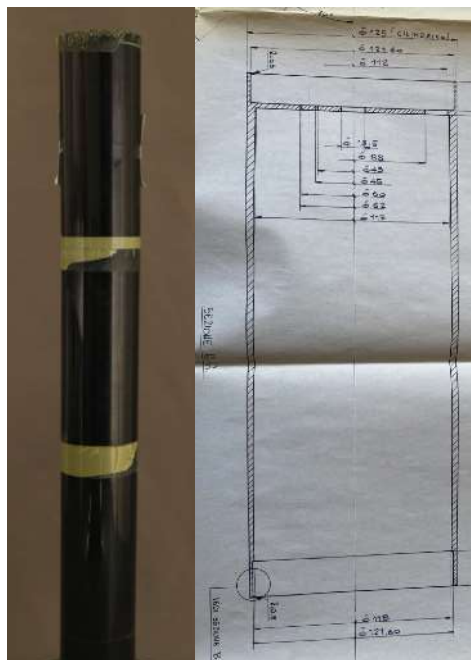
De gauche à droite : photographie détaillée de la colonne du portemanteau Planta, plan technique des segments de la colonne. ©Z.Pacreau.
